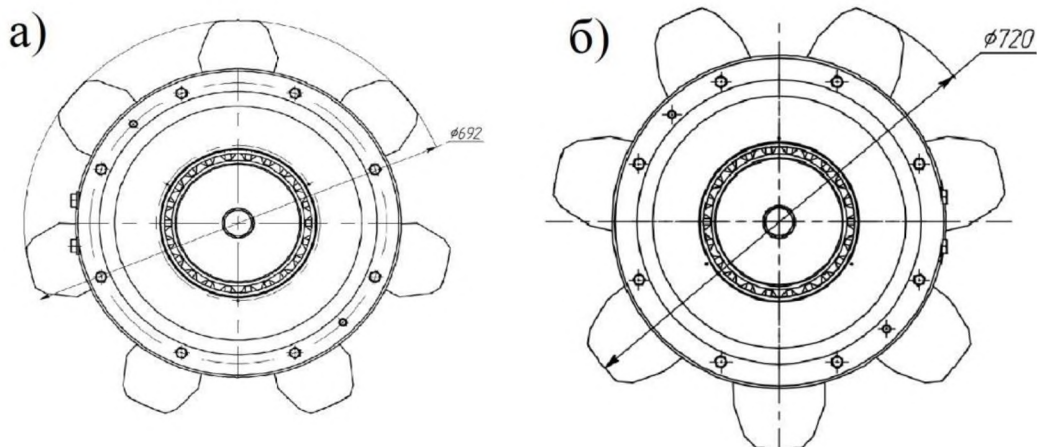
Приводные колеса: а) А-3810; б) А-4210
